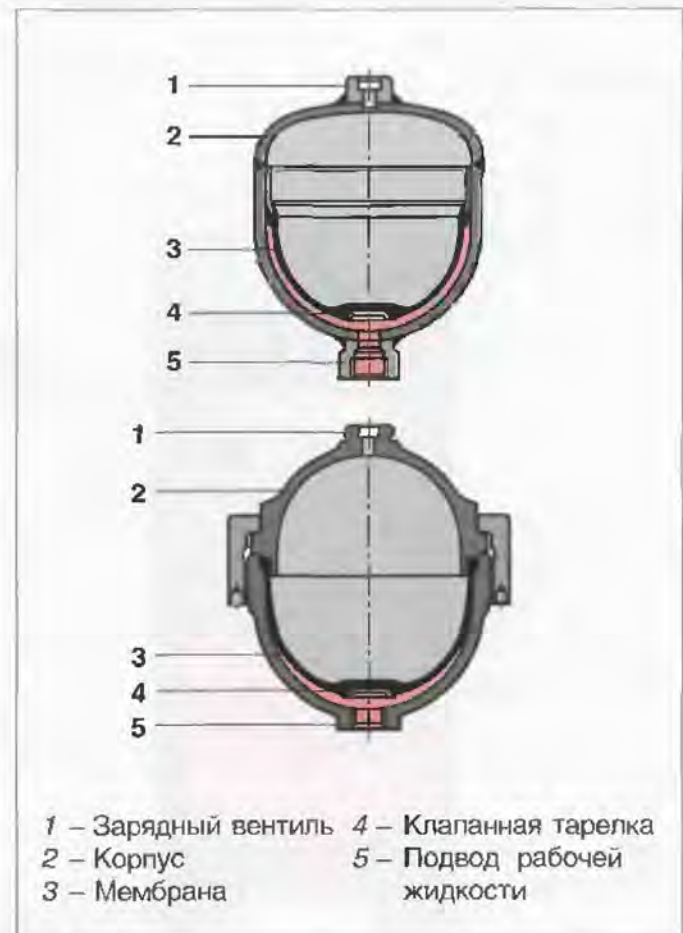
Мембранный аккумулятор: вверху – сварная конструкция; внизу – разборная
